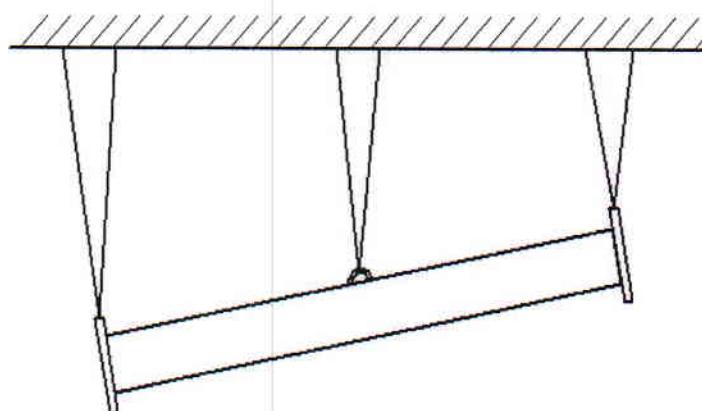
(а) Схема навески длинномерных (6-12м) заготовок с фланцами:
